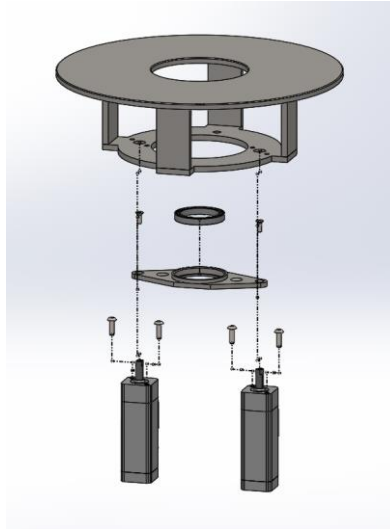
Modelo de ensamble 3D realizado en Solidworks.
